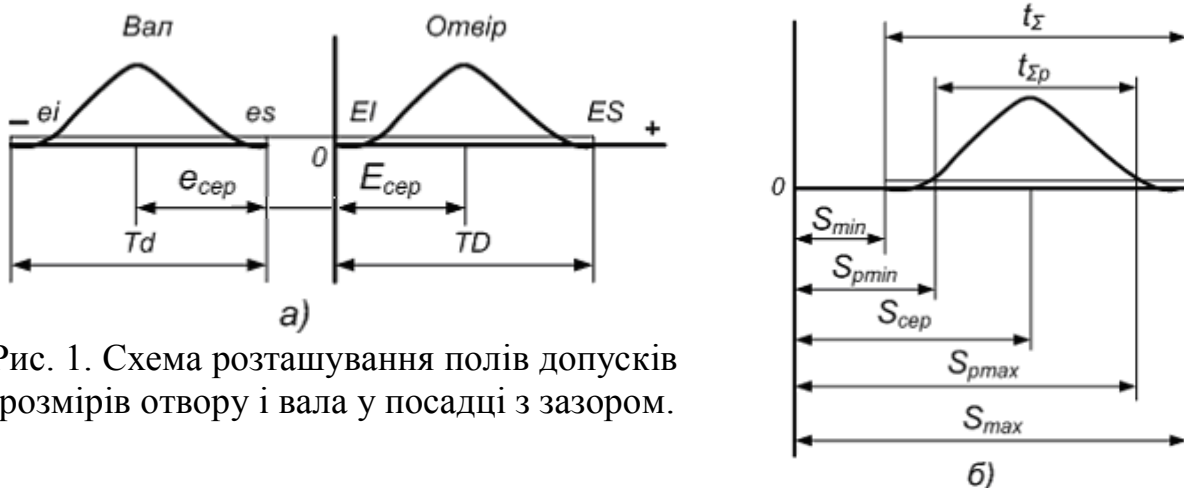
Схема розташування полів допусків розмірів отвору і вала у посадці з зазором.
